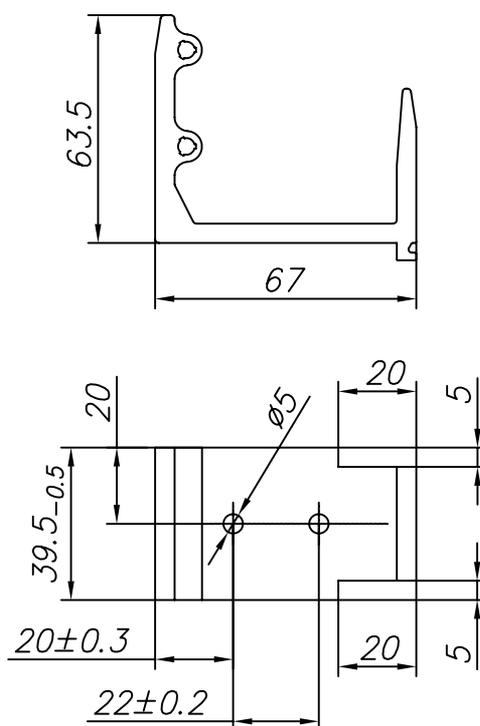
Изготовление соединителя FLGU.400.0912
